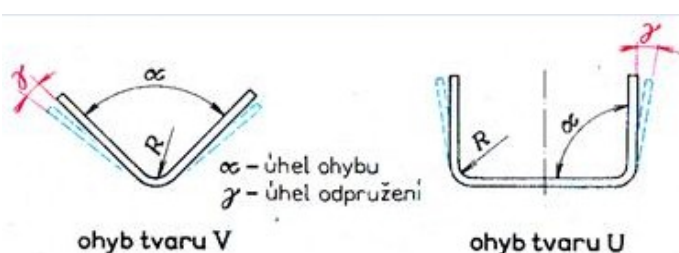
Ohýbání do tvaru a) „V“, b) „U“. [3]
